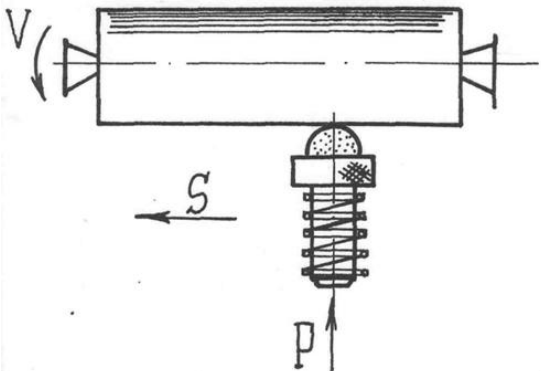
Обработка выглаживанием наружной цилиндрической поверхности заготовки на токарном станке [90].
